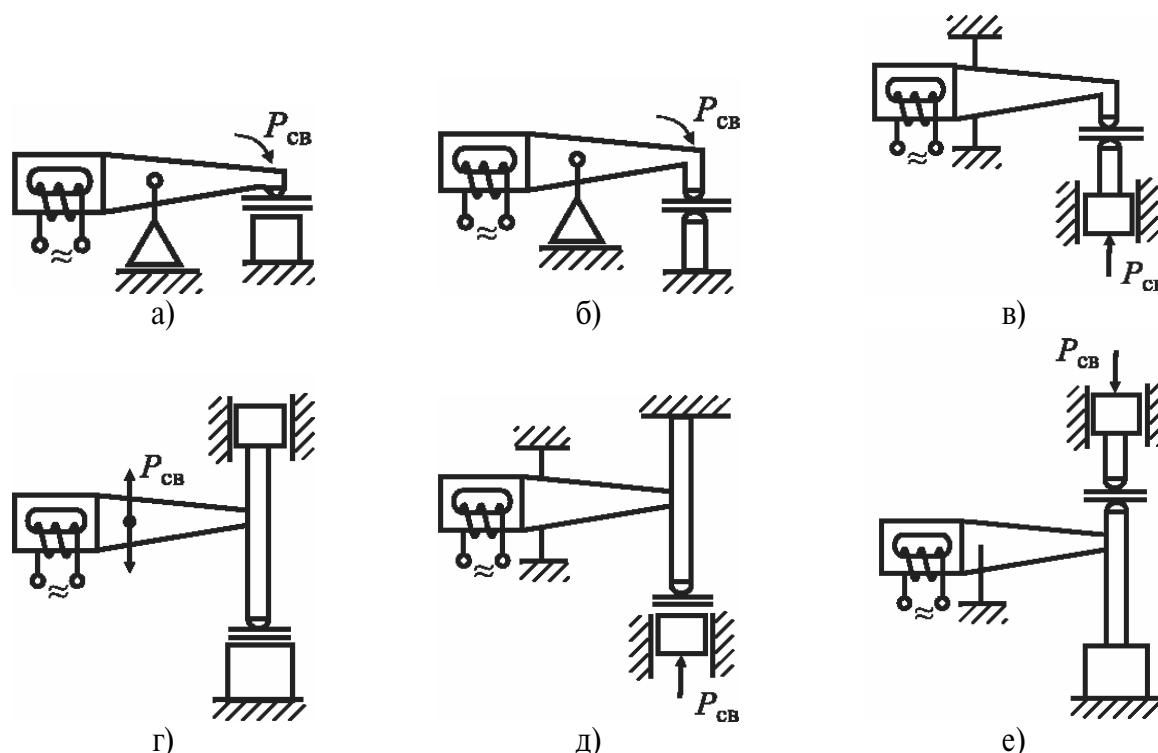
Принципиальные кинематические схемы машин для ультразвуковой сварки металлов
